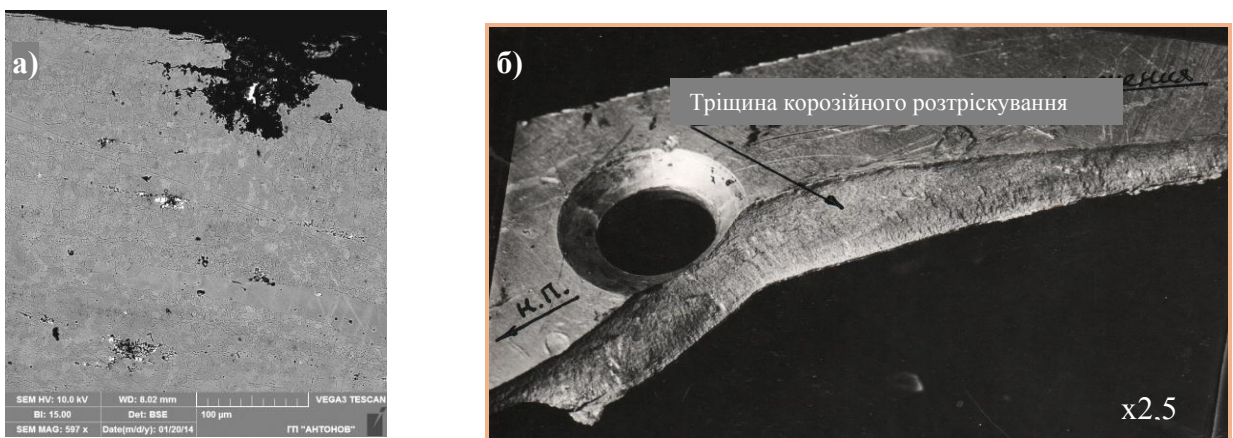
Ушкодження поверхні обшивки внаслідок виразкової корозії (а); наскрізне руйнування обшивки за механізмом корозійного розтріскування (б).
